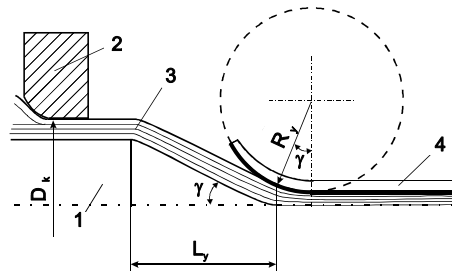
Первичная приформовка стойки профиля: 1 – оправка; 2 – калибрующая фильера; 3 – формируемый материал; 4 – формирующее устройство
